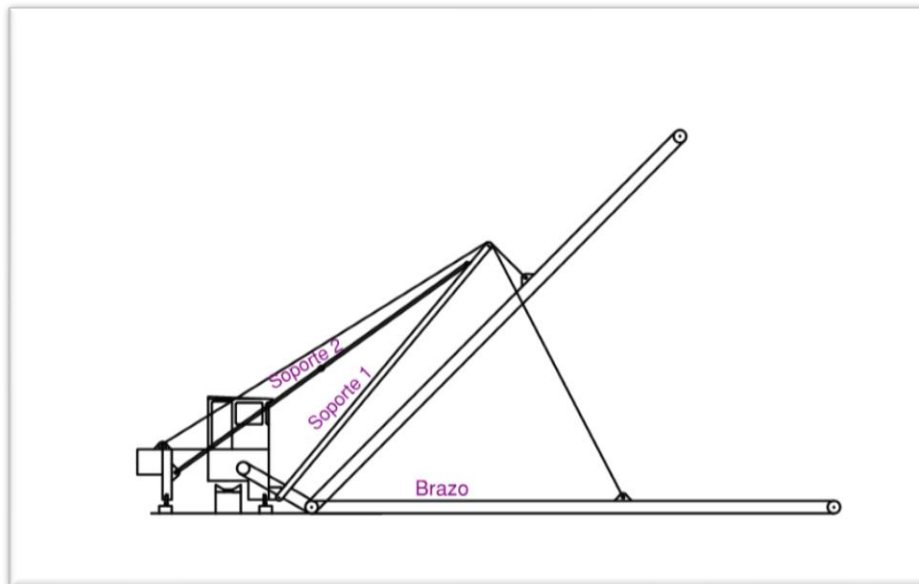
Elementos del reclamador bajo análisis estático (Fuente: Autores)
